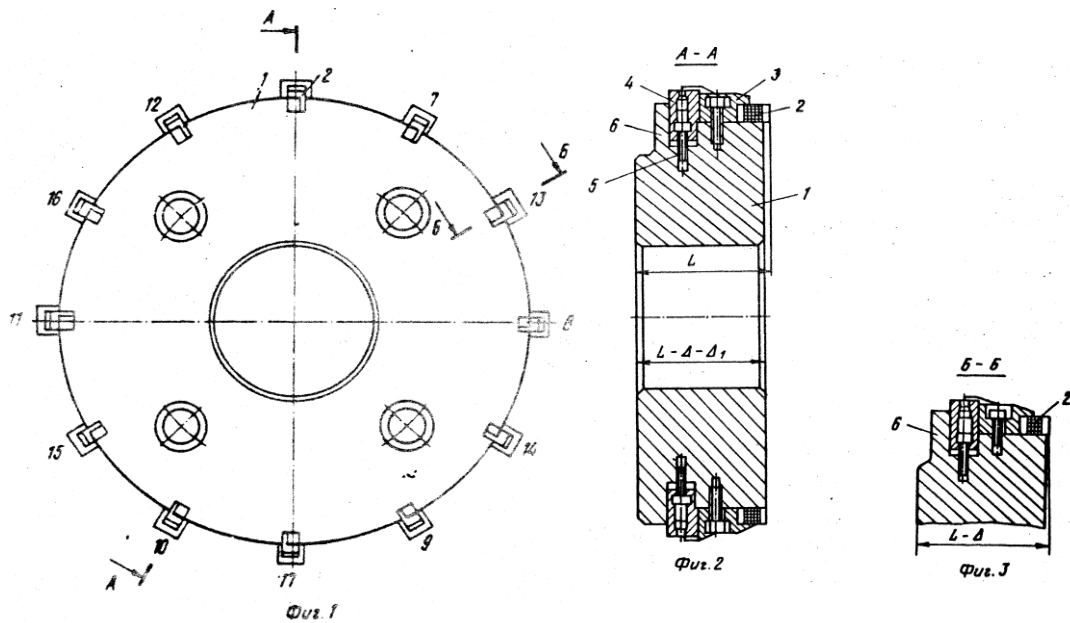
Торцева фреза по а.с. 1174177 МКИ В 23 С 5/06
